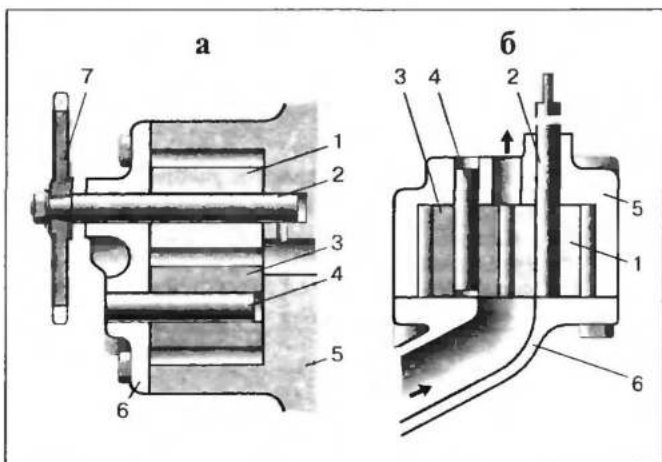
Масляные насосы с шестернями наружного зацепления: а — с приводом цепью; б — традиционной схемы с приводом от дополнительного вала; 1 — ведущая шестерня; 2 — ведущий валик; 3 — ведомая шестерня; 4 — ось; 5 — корпус; 6 — крышка; 7 — звездочка привода
